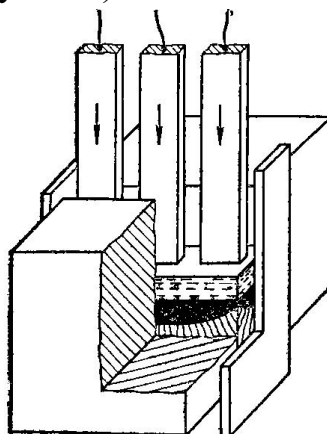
Схема электрошлаковой сварки пластинчатым электродом
